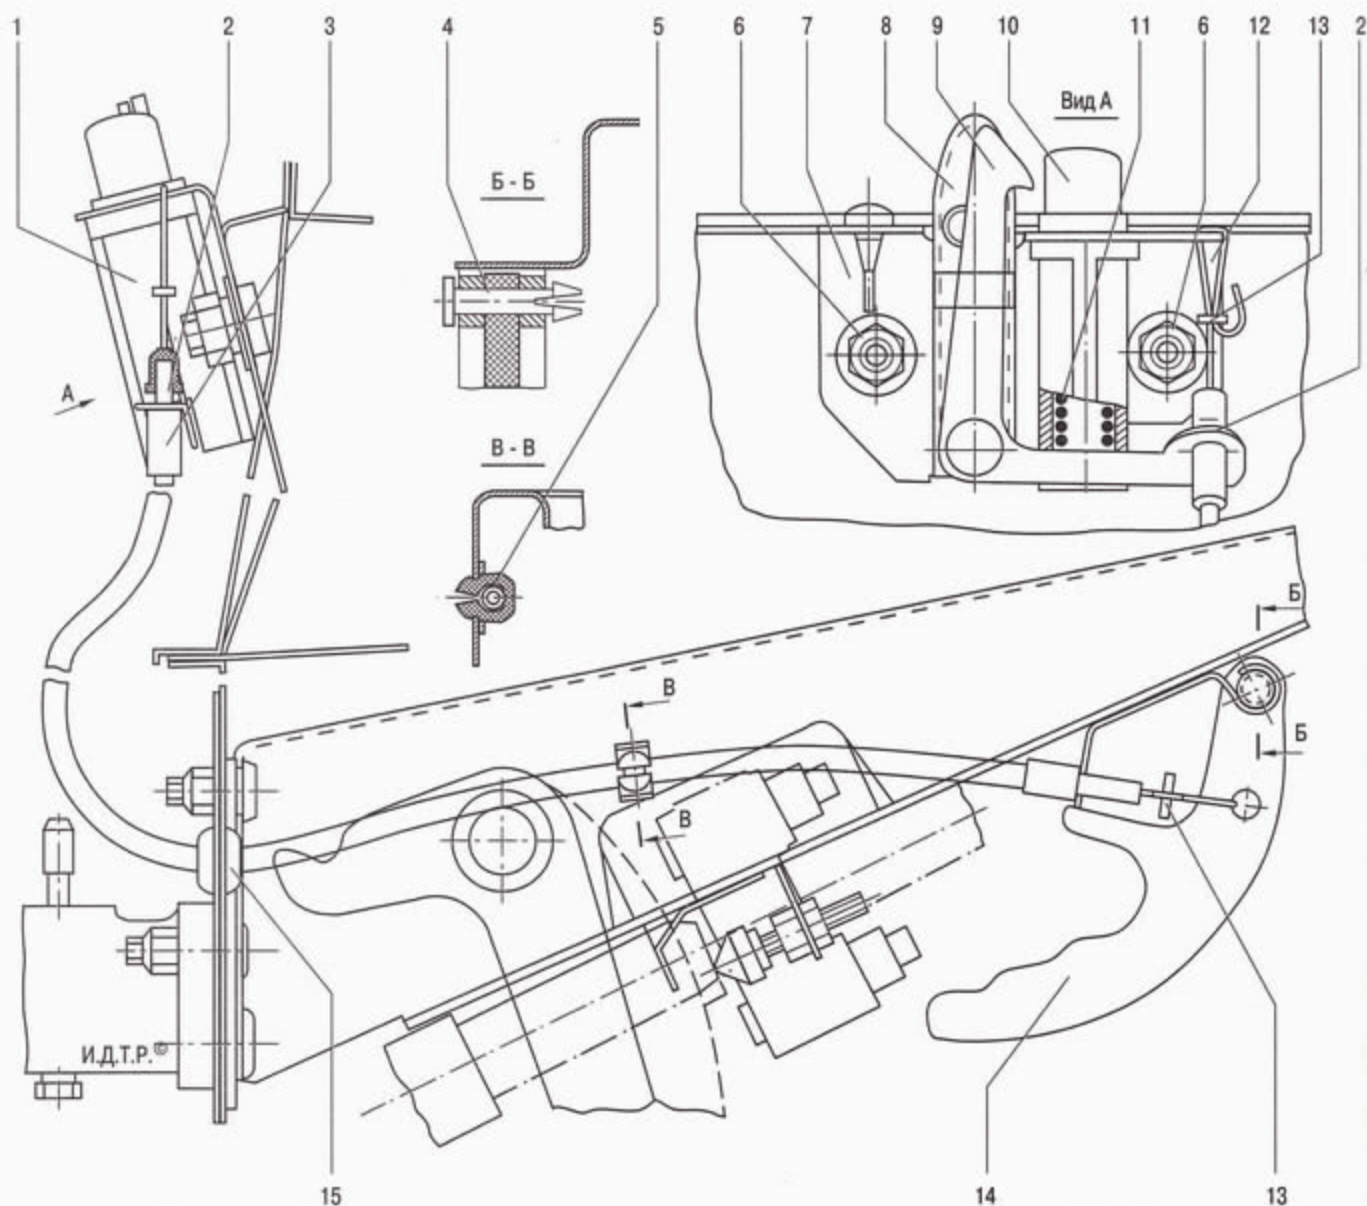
Замок капота и его привод: 1 – замок; 2 – упор; 3 – оболочка тяги; 4 – ось рукоятки привода замка капота; 5 – скоба крепления оболочки; 6 – гайка; 7 – корпус замка; 8 – направляющий штырь; 9 – крючок защелки; 10 – толкатель; 11 – пружина; 12 – тяги; 13 – шайба; 14 – рукоятка привода замка капота; 15 – втулка
